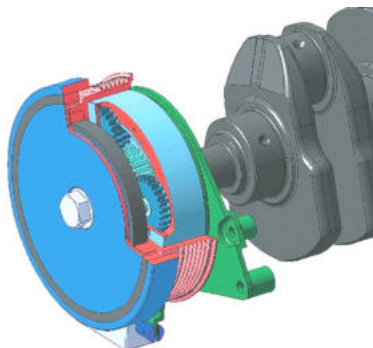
Размещение планетарного редуктора на коленчатом валу двигателя
